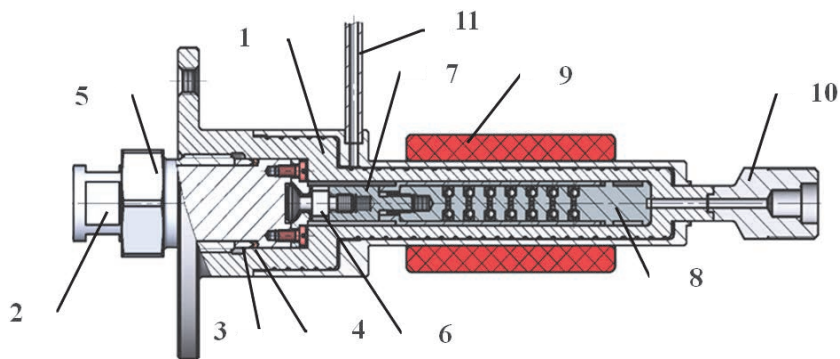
Конструкция камеры заполнения системы НСОМД: 1 – кожух камеры в сборе; 2 – крышка; 3 – кольцо упорное; 4 – прокладка; 5 – гайка; 6, 7 – винт; 8 – кассета в сборе; 9 – нагреватель; 10 – штуцер для подачи газа; 11 – трубопровод для откачки продифундировавшего газа
